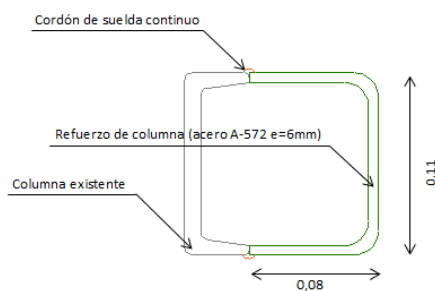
Detalle de refuerzo de Parante trasero de Contenedor
